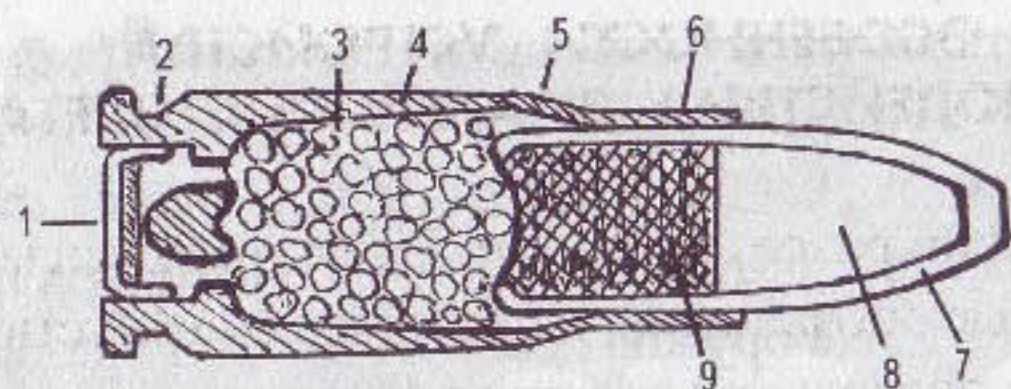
Разрез патрона МПЦ калибра 5,45 мм к пистолету ПСМ: 1 — капсуль; 2 — кольцевая проточка гильзы; 3 — пороховой заряд; 4 — корпус гильзы; 5 — скат; 6 — дульце гильзы; 7 — оболочка пули; 8 — стальной сердечник; 9 — свинцовая заливка
